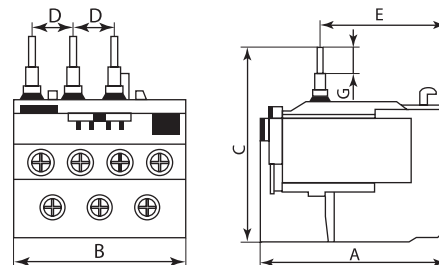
Габаритные и установочные размеры реле РТЛ-1001...РТЛ-1003
